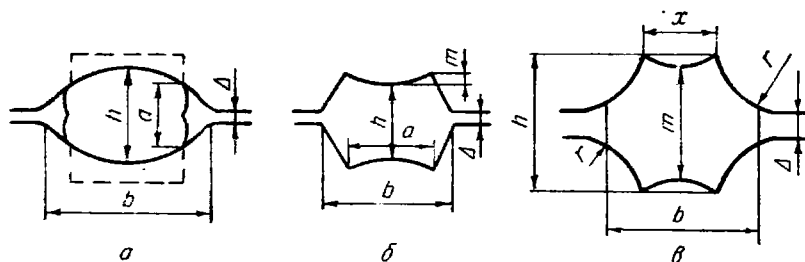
Обозначения размеров калибров для прокатки шестигранной стали: a — овальный калибр; b — предотделочный калибр; $в$ — предчистовой шестигранный калибр
